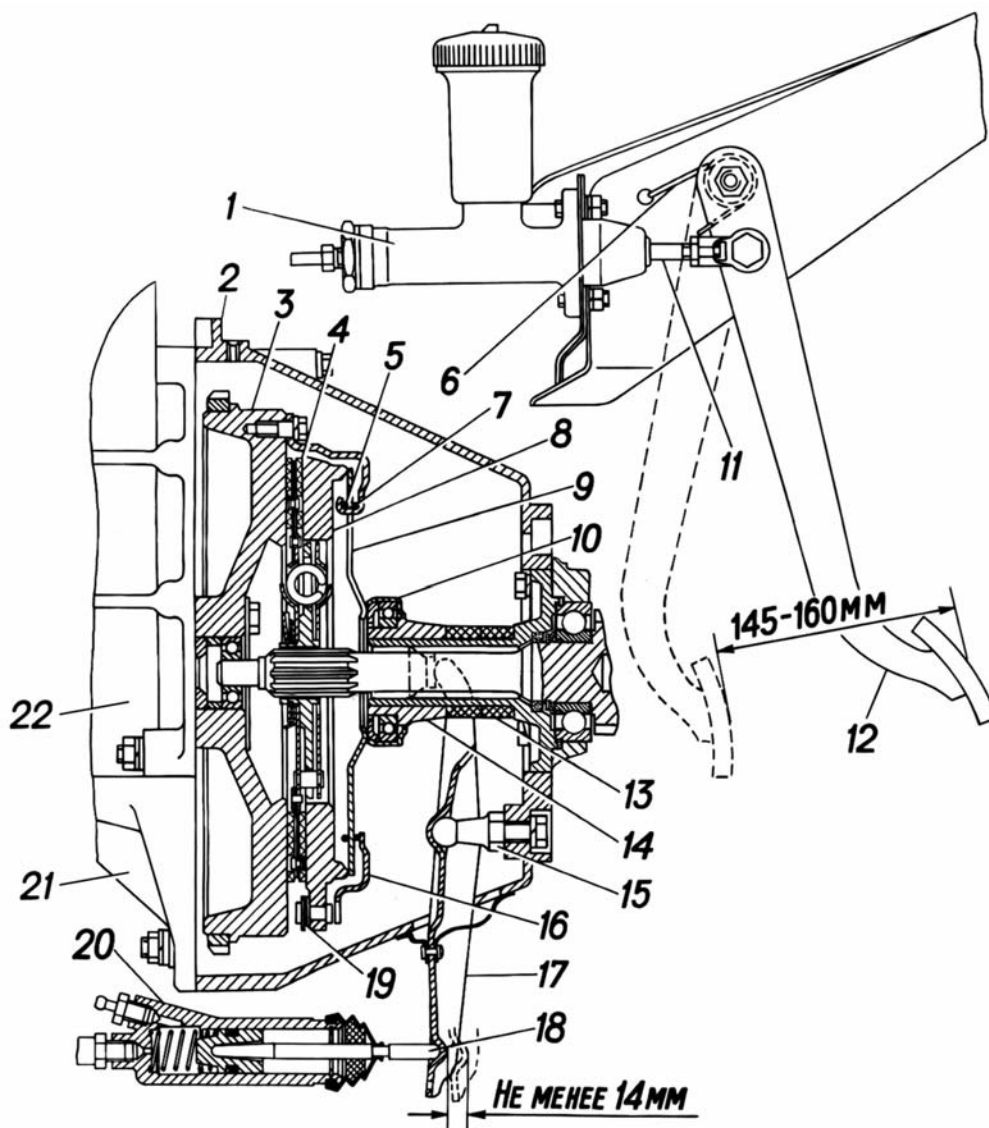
Сцепление и привод выключения сцепления: 1 - главный цилиндр выключения сцепления; 2 - картер сцепления; 3 - маховик; 4 - ведомый диск сцепления; 5 и 7 - опорные кольца; 6 - оттяжная пружина педали; 8 - нажимной диск; 9 - пружина нажимная диафрагменная; 10 - подшипник выключения сцепления; 11 - толкатель главного цилиндра; 12 - педаль; 13 - поролоновые кольца; 14 - муфта выключения сцепления; 15 - шаровая опора; 16 - кожух; 17 - вилка выключения сцепления; 18 - толкатель рабочего цилиндра; 19 - пластины соединительные; 20 - рабочий цилиндр; 21 - усилитель; 22 - блок двигателя
